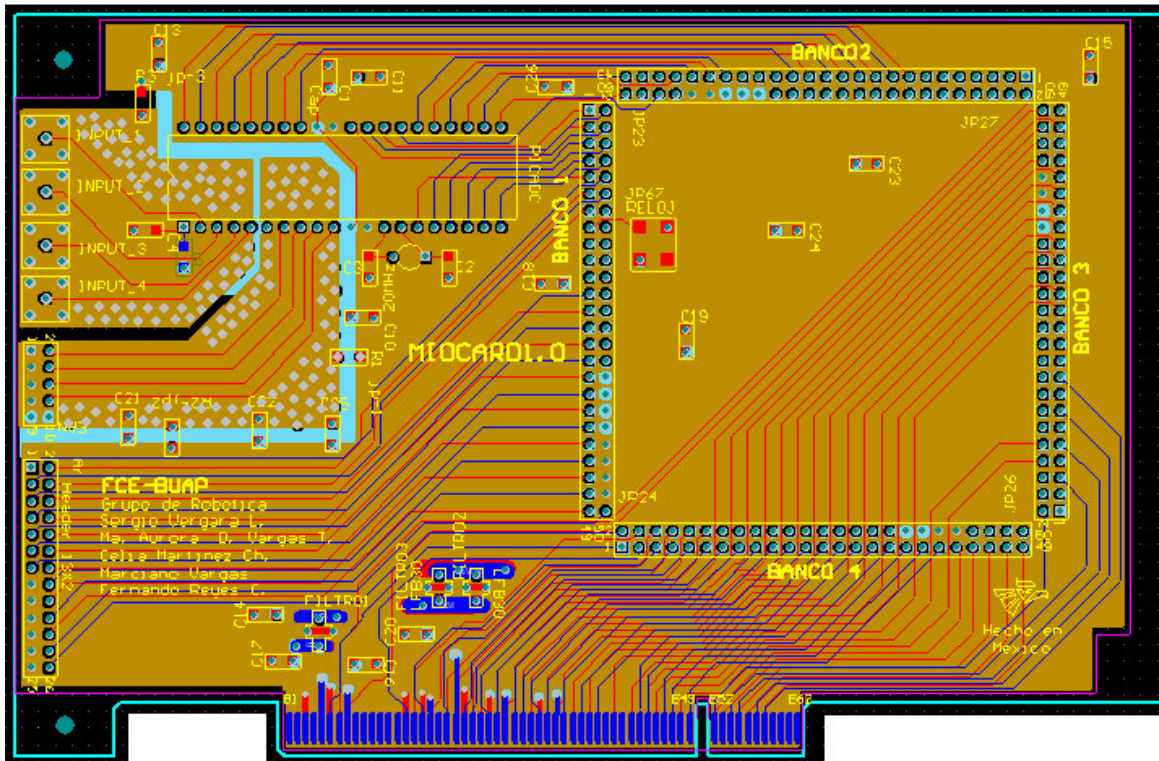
Diseño PCB de Tarjeta de adquisición MIOCARD 1.0
